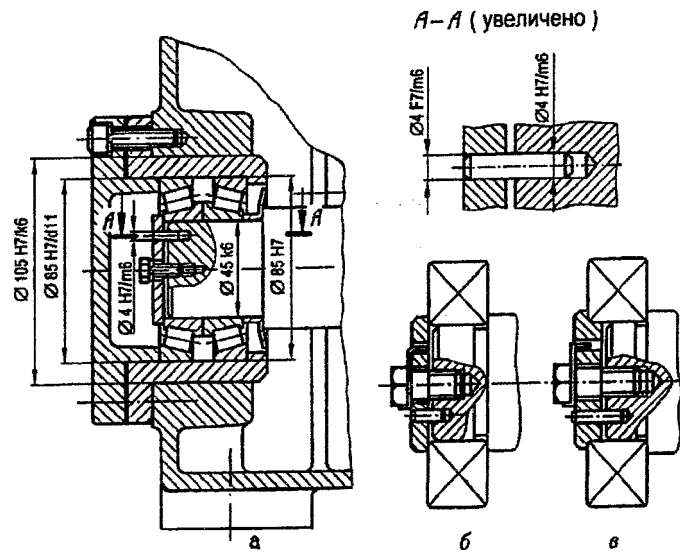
Пример конструкции подшипникового узла с деталями для регулирования осевого зазора в подшипниках и крепления их внутренних и наружных колец
